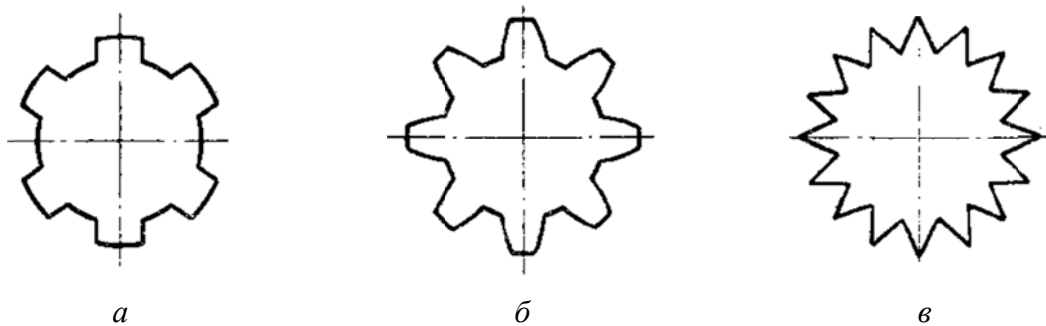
Основные типы зубчатых (шлицевых) соединений:
